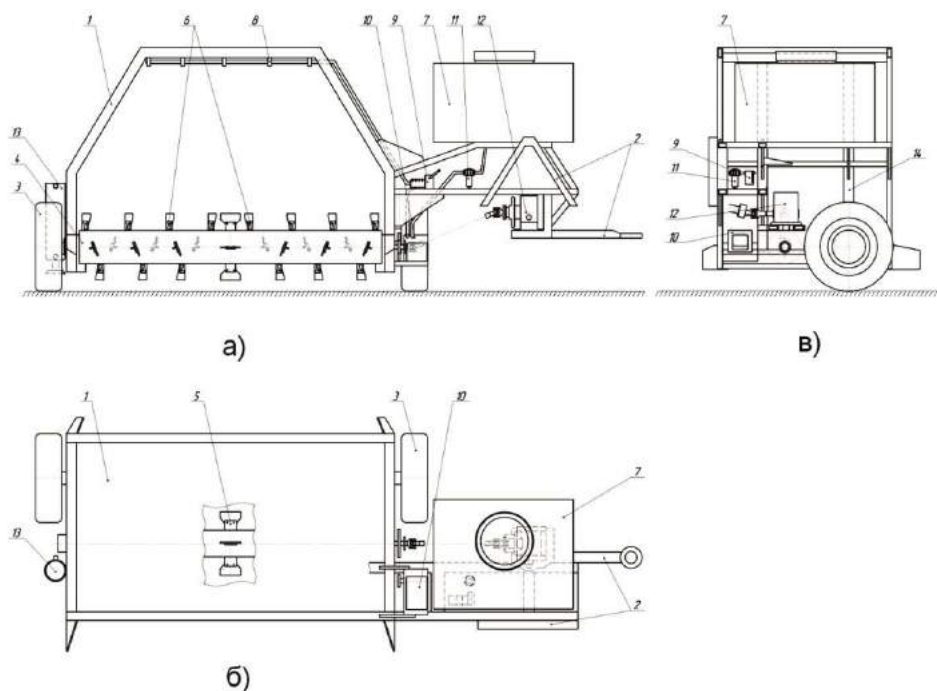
Конструктивна схема змішувача–аератора компосту: а – вид спереду, б – зверху, в – справа; 1 – рама; 2 – зчіпка; 3 – опорні колеса; 4 – фрезерний обертовий барабан з робочими елементами; 5, 6 – плоскі лопаті; 7 – місткість для рідких компонентів; 8 – розпилювачі; 9 – розподільник; 10 – насос; 11 – фільтр; 12 – редуктор; 13 – гідродомкрат; 14 – гвинтові вали
